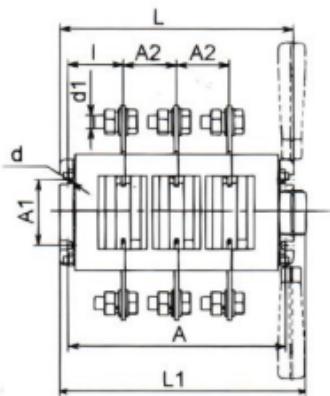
Выключатель-разъединитель на два направления трехполюсный с боковой рукояткой
